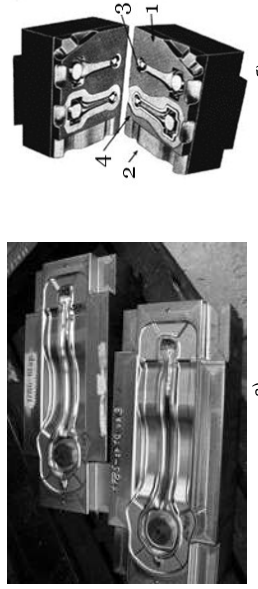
Штамп. а) – підкладний – однорічковий; б) молотовий – багаторічковий; 1, 2, 3, 4 – річкові штампа
